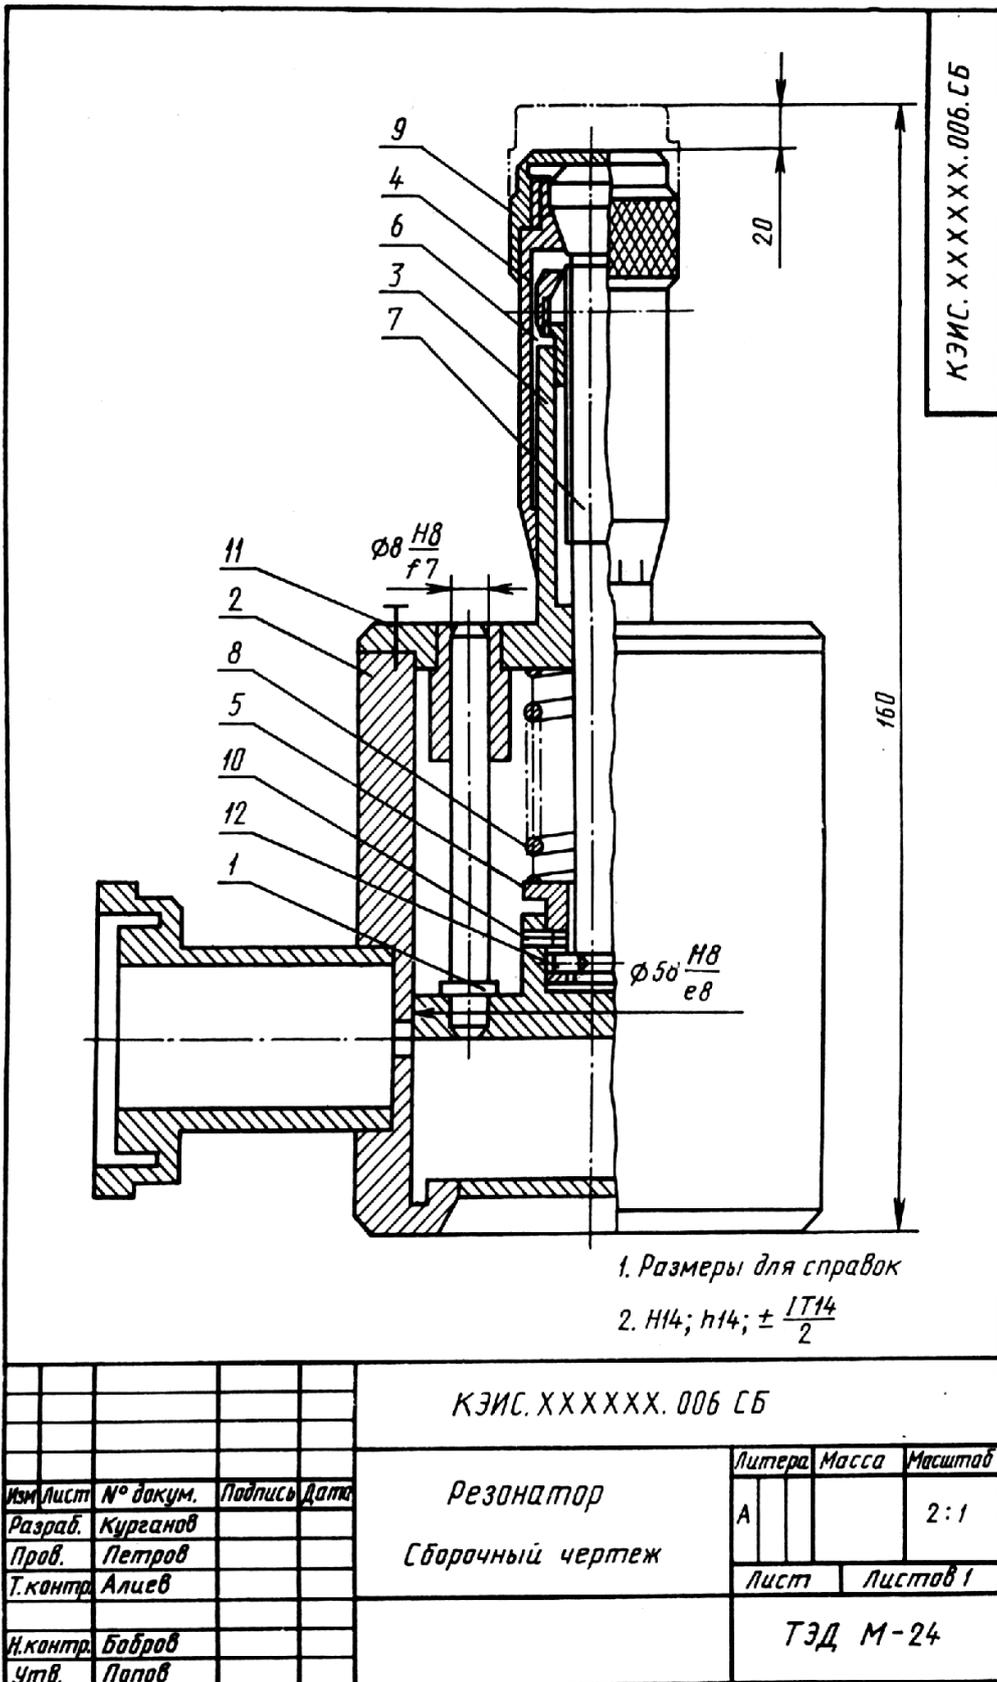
Пример выполнения сборочного чертежа резонатора
